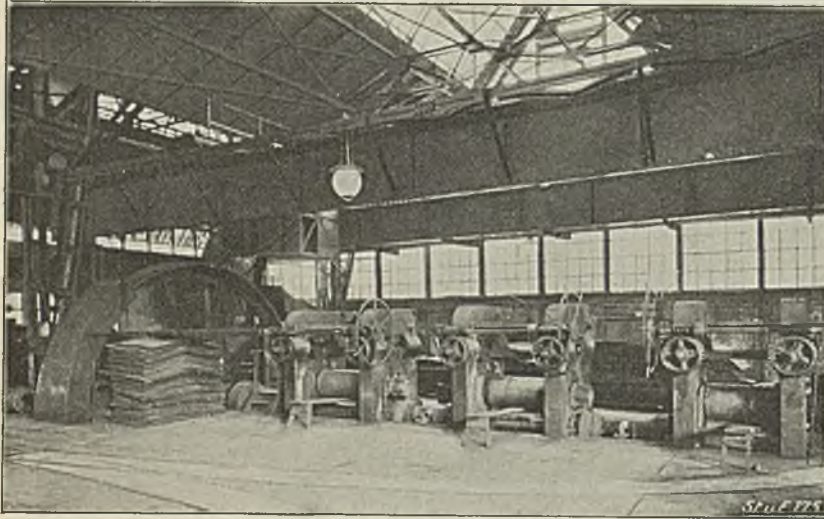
Dressierstrecke im Feinblechwalzwerk.
